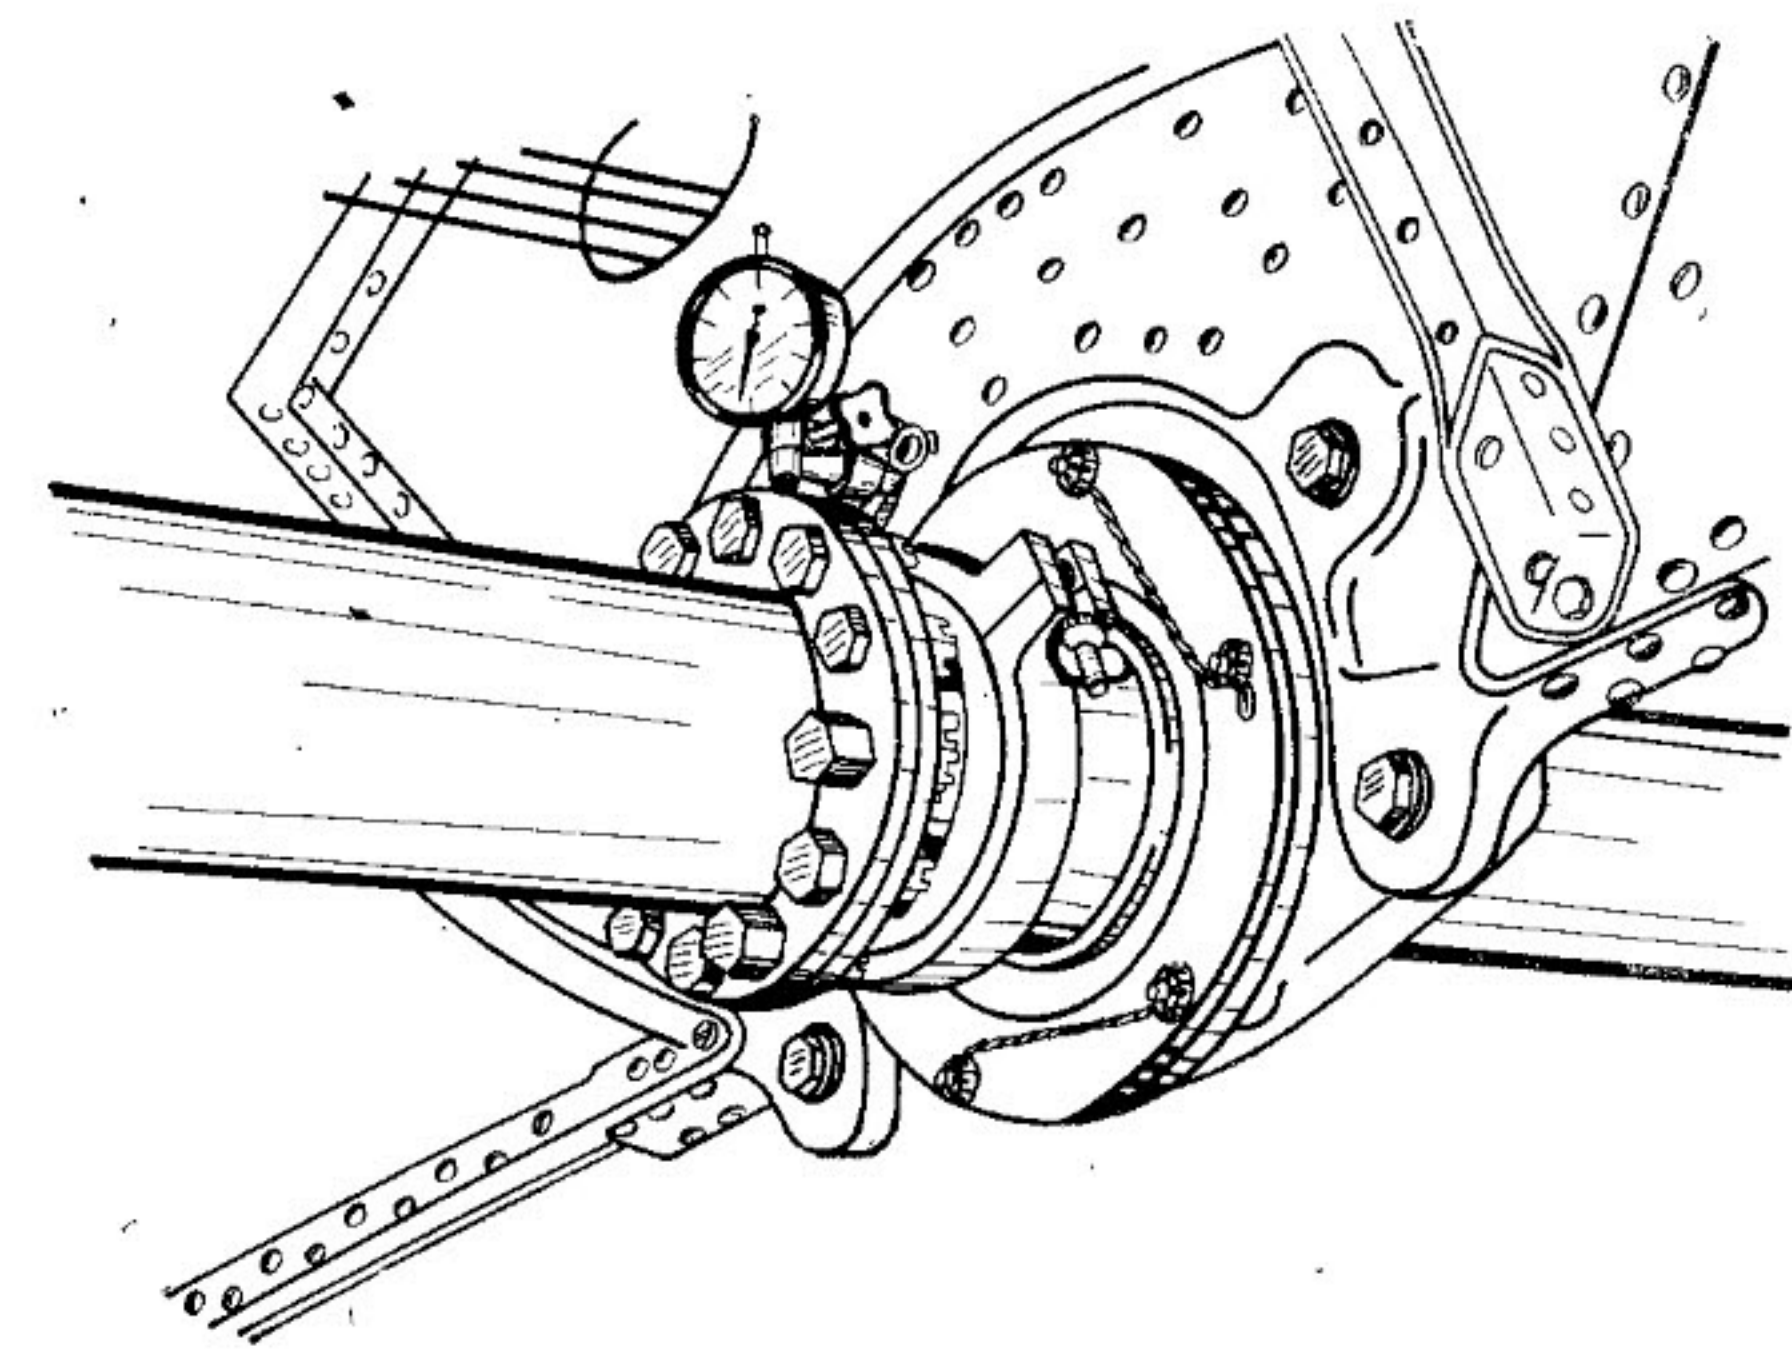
Установка приспособления для замера перекосов осей хвостового вала и перекоса опор подшипников хвостового вала
